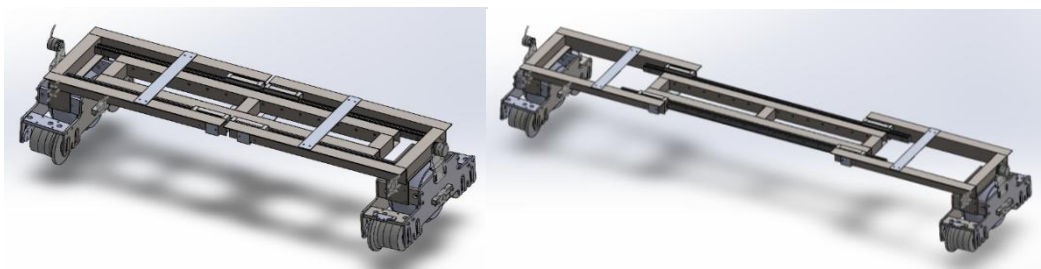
Diseño A del carro de ultrasonidos en posición métrica e ibérica. Fuente: Propia
